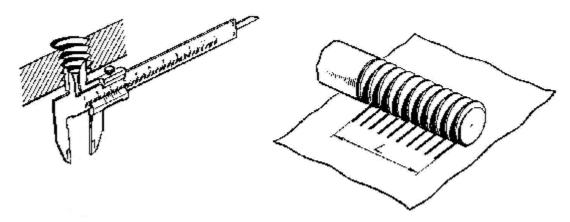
Измерение внутреннего диаметра резьбы d_1 штангенциркулем
